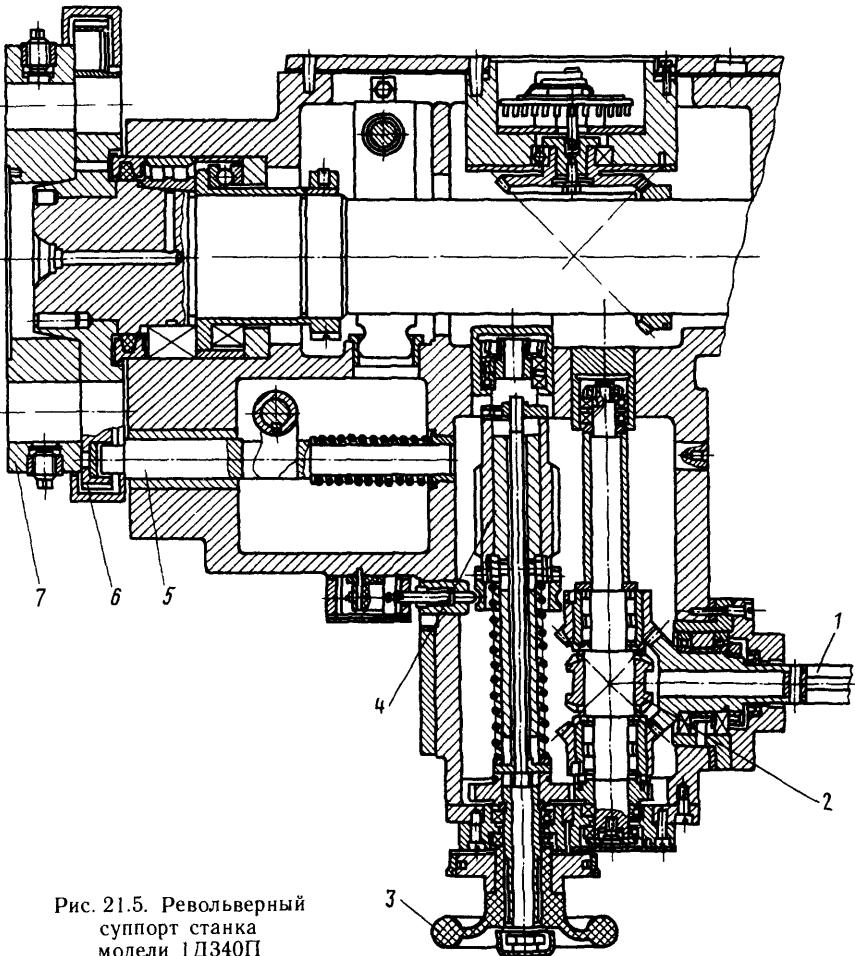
Револьверный суппорт станка модели 1Д340П
